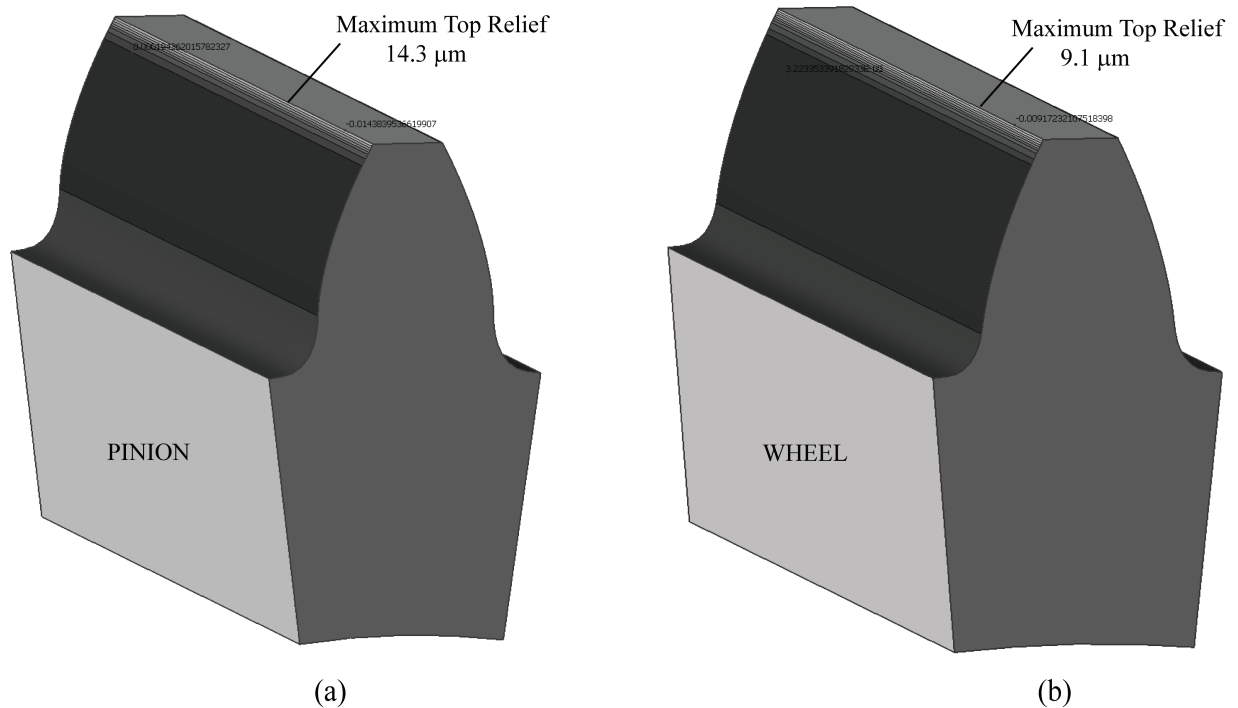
Comparación de los mejores relieves modificados para el diseño optimizado del (a) piñón y (b) de los miembros de la rueda del diseño de conjunto de engranajes.
